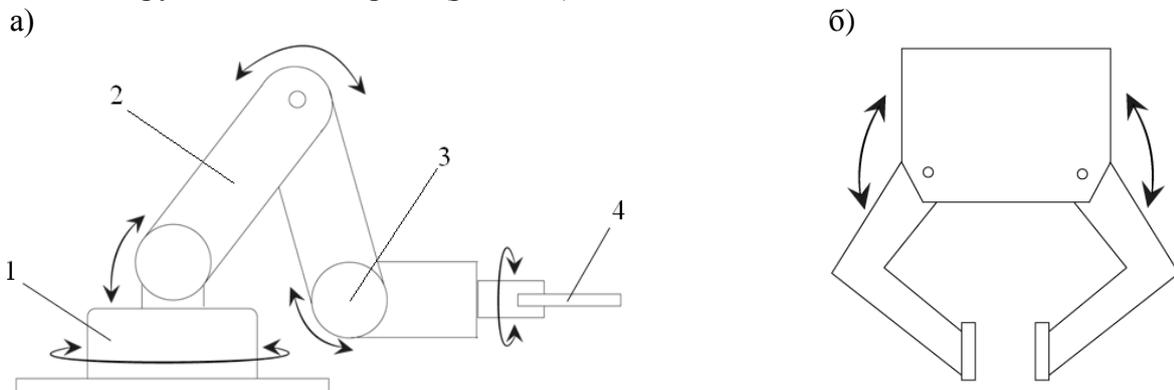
Внешний вид манипулятора: а – манипулятор, б – грузозахватный орган, 1 – поворотная платформа, 2 – звено, 3 – шарнир, 4 – грузозахватный орган
